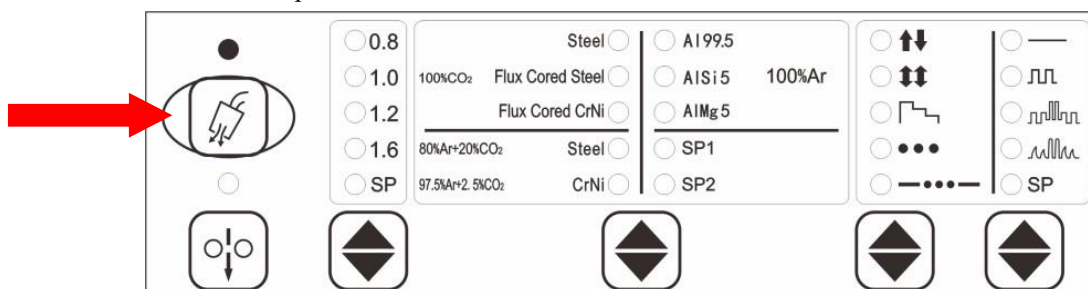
Кнопка "Проверка подачи газа" на панели управления сварочного источника питания
